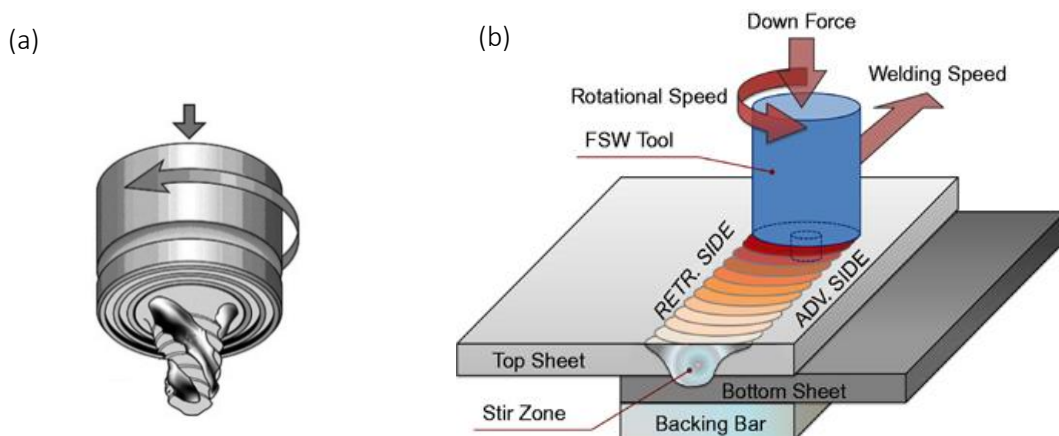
(a) Ferramenta de FSW [17], (b) Esquema do processo FSW [18].
